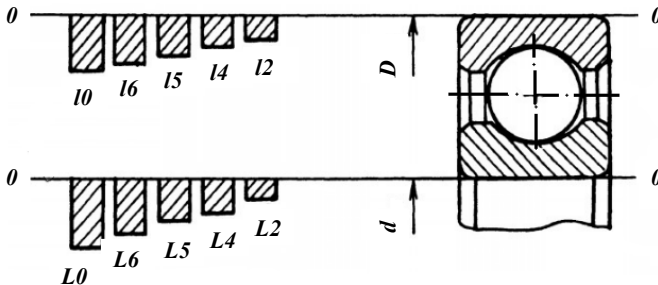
Схема расположения полей допусков наружного и внутреннего колец подшипника качения
